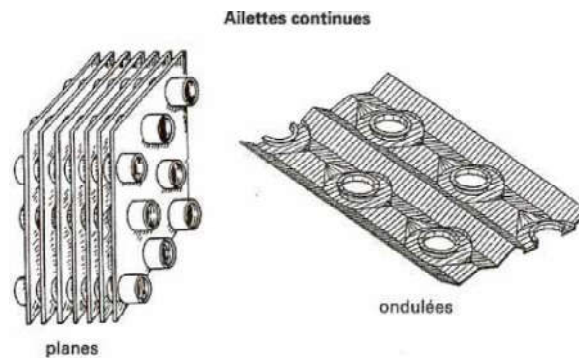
Ailettes continues ou indépendantes pour tubes[8].
